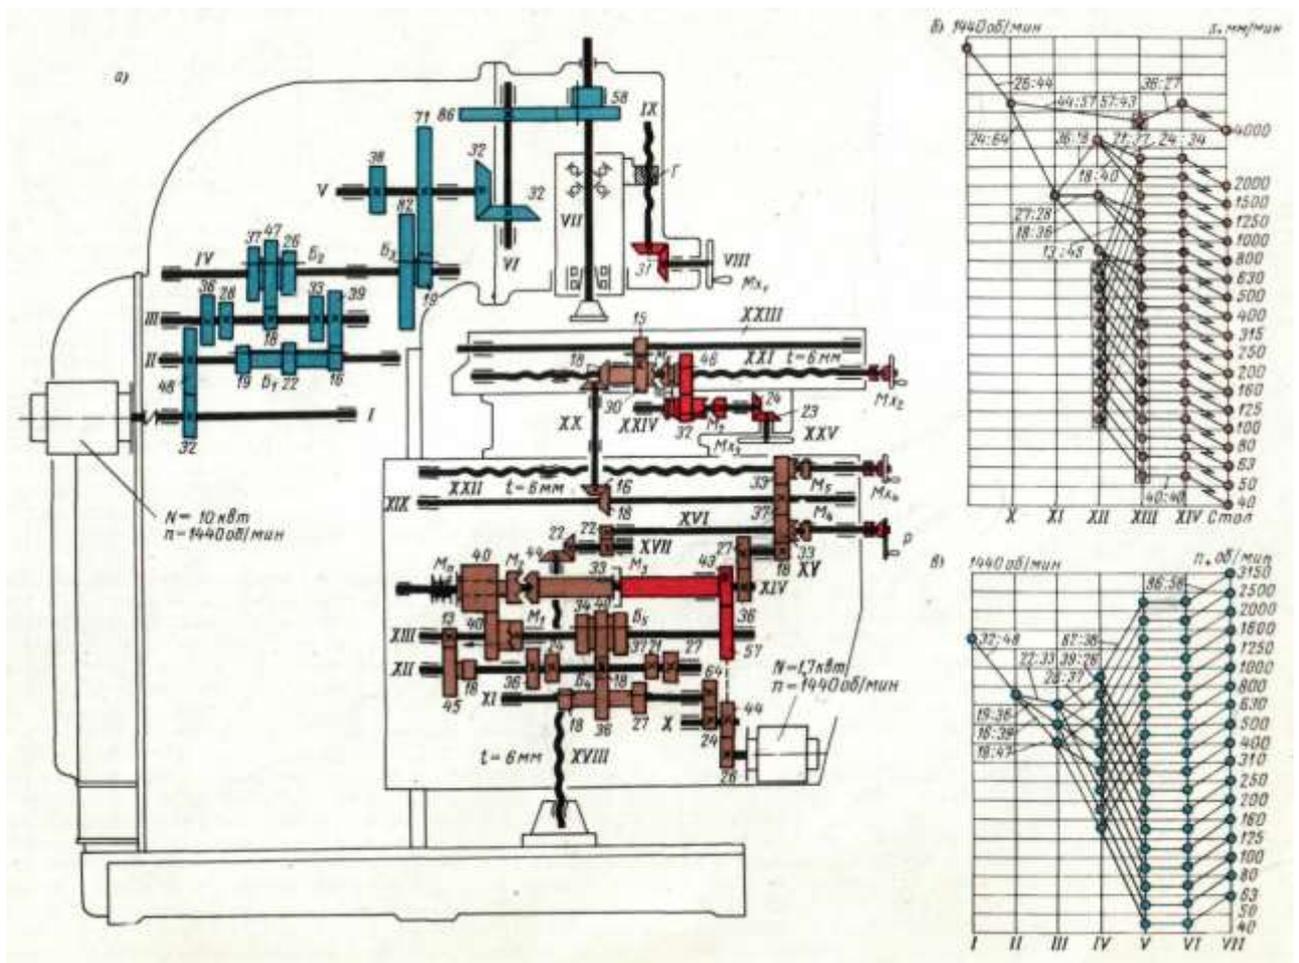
Кинематическая схема вертикально-фрезерного станка модели 6N12PB
